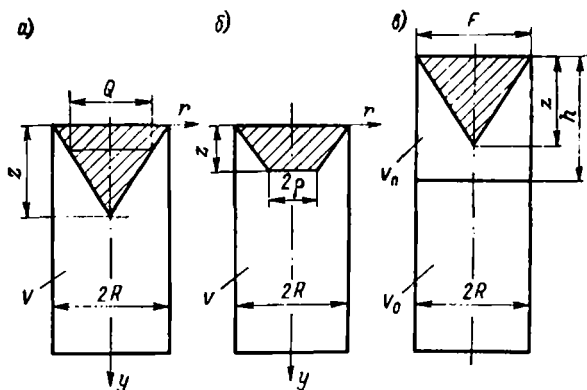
Схемы к расчетам областей усадочных раковин: а — отливка из чистого металла; б — отливка из сплава, кристаллизующегося в широком интервале температур; в — отливка с прибылью
